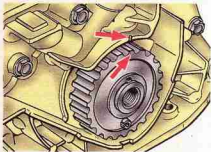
Проверка совпадения установочных меток на шкиве распределительного вала и задней защитной крышке
